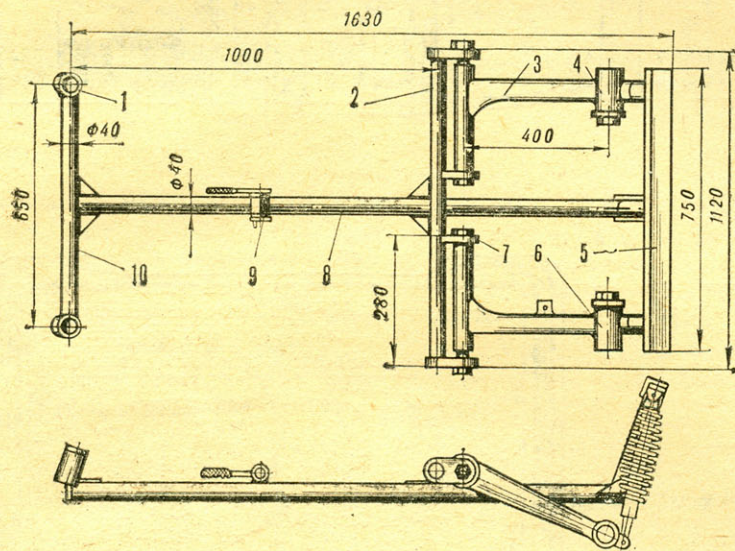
Рама: 1 — шарнир передней поворотной цапфы, 2 — задняя поперечина, 3 — маятник задней подвески, 4 — втулка крепления правого колеса, 5 — опора амортизаторов задней подвески, 6 — втулка крепления ведущего колеса, 7 — проушины крепления маятников, 8 — основная труба хребтовой рамы, 9 — узел крепления рукоятки заводки двигателя, 10 — передняя поперечина.
